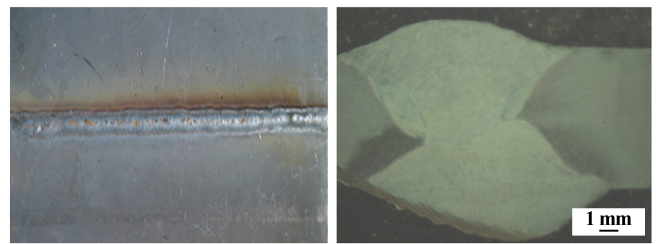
热输入 70 kJ/cm 焊接接头宏观形貌
